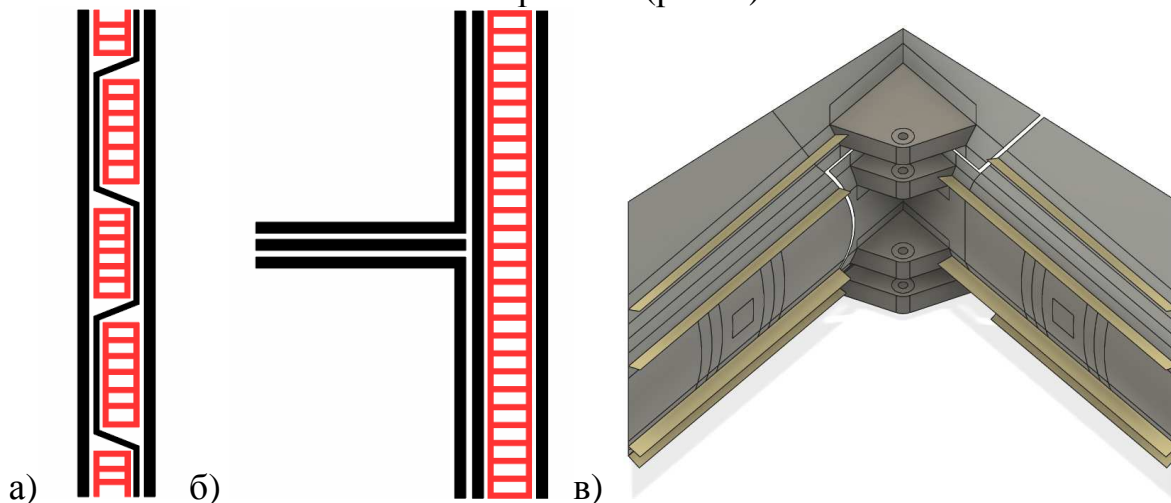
Схематичное изображение конструкции отвала: а – вертикальные внутренние рёбра жёсткости (вид сверху); б – горизонтальные внешние рёбра жёсткости (вид сбоку); в – общий вид
